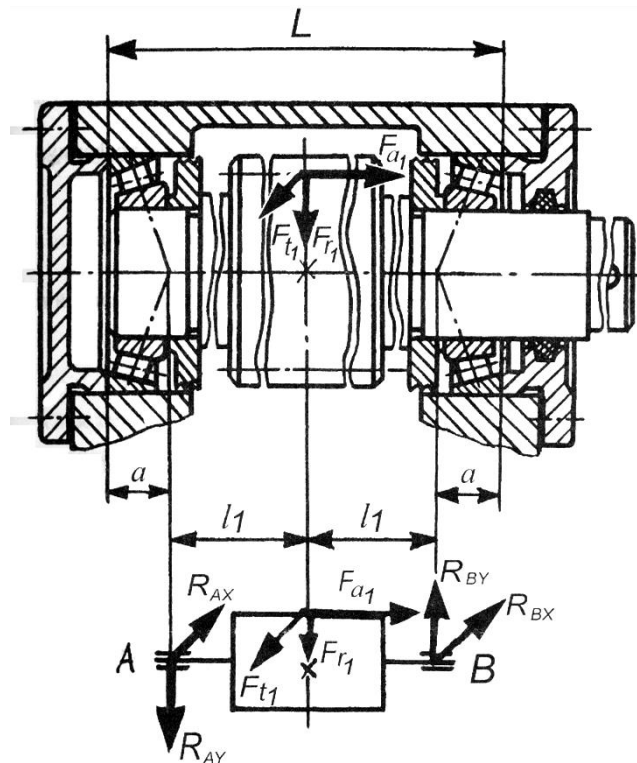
Подшипниковые узлы вала червяка червячного редуктора с верхним расположением червяка
